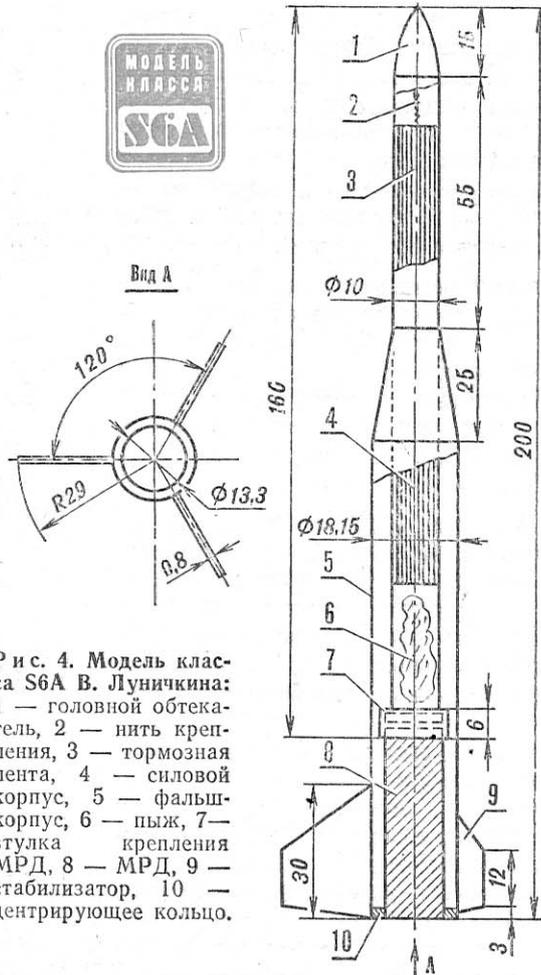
Модель класса S6A В. Луничкина: 1 — головной обтекатель, 2 — нить крепления, 3 — тормозная лента, 4 — силовой корпус, 5 — фальшкорпус, 6 — пьез, 7 — втулка крепления МРД, 8 — МРД, 9 — стабилизирующее кольцо.
